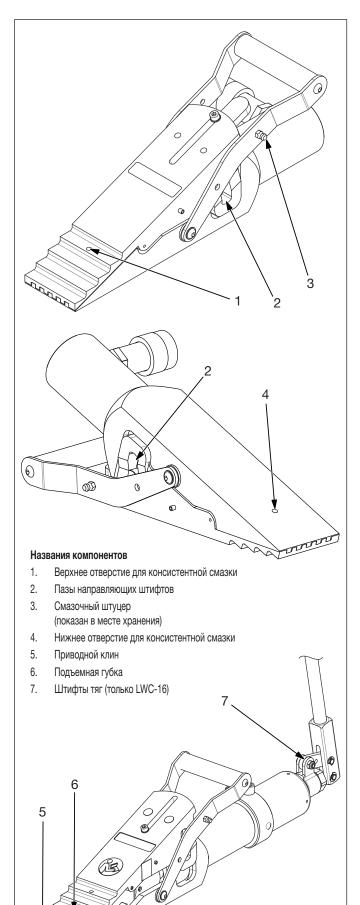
Смазка, модели LW-16 и LWC-16
